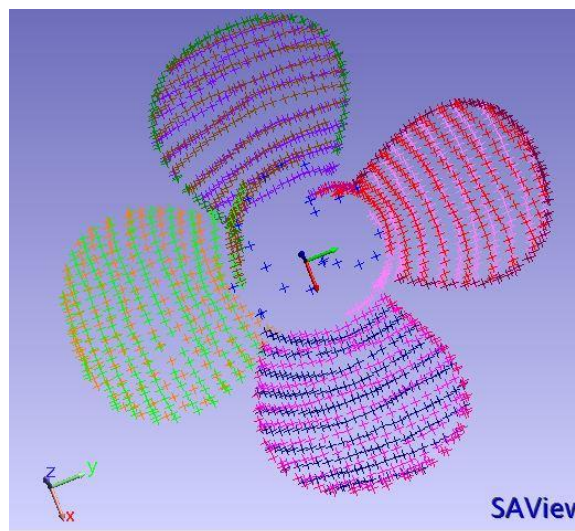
Вихідна 3D-модель заготовки ГВ Ік-7
